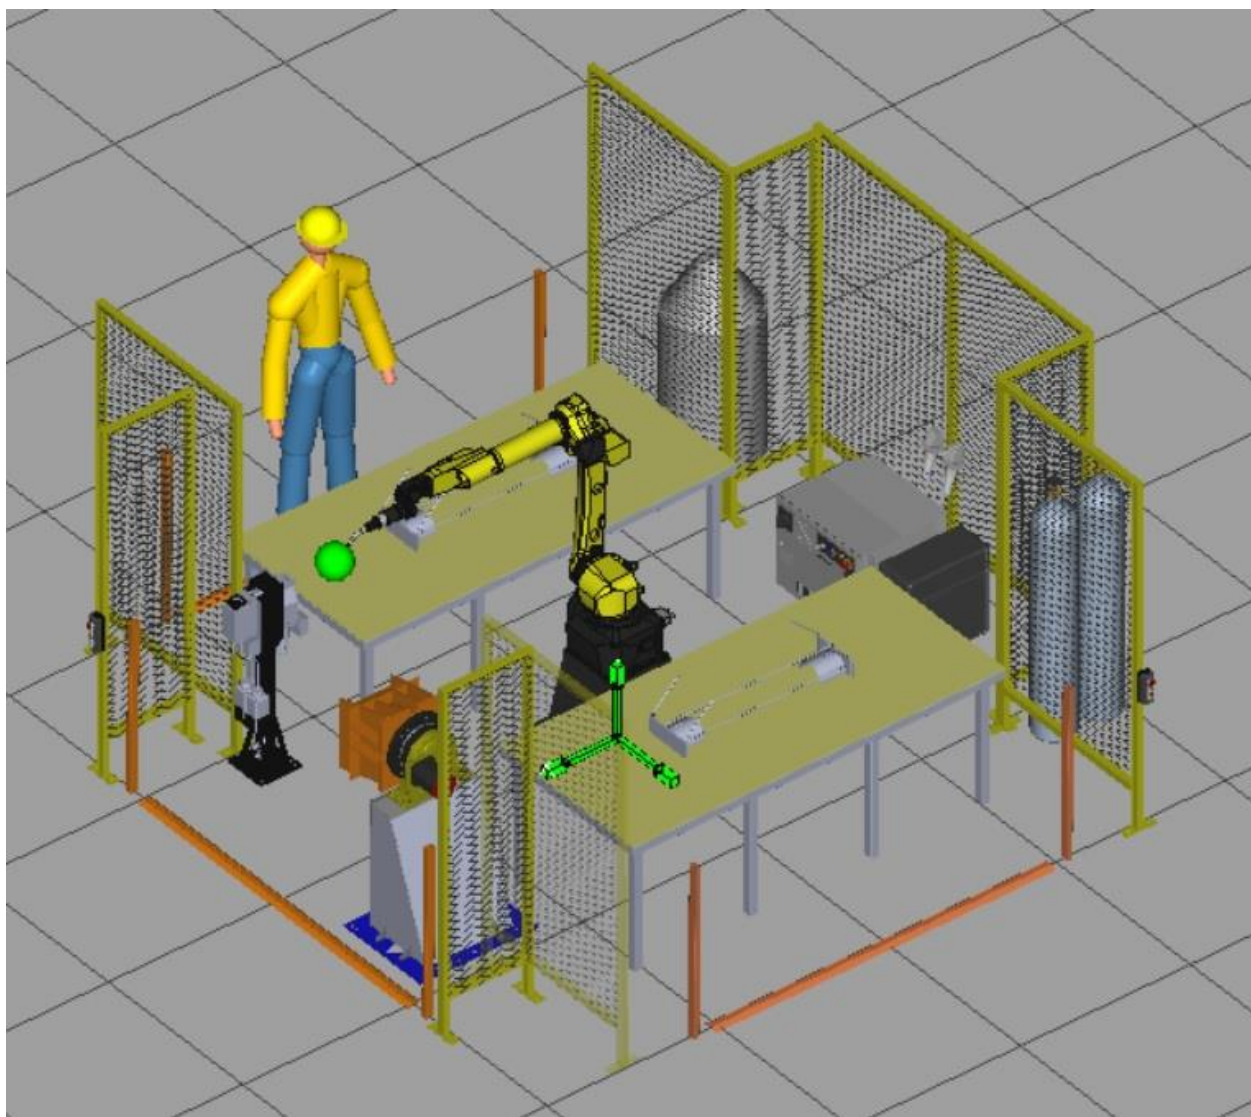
Загальний вигляд роботизованого зварювального поста.
